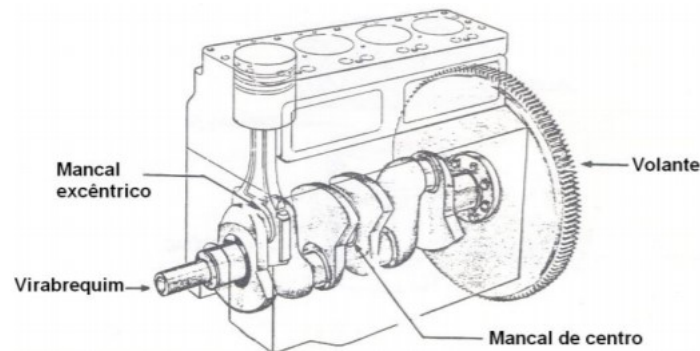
Desenho esquemático do virabrequim e do volante de inércia
